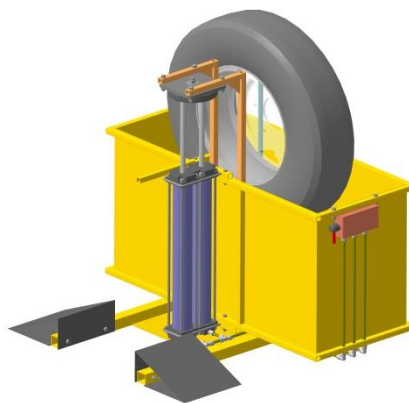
Ванна для проверки герметичности колес и шин
